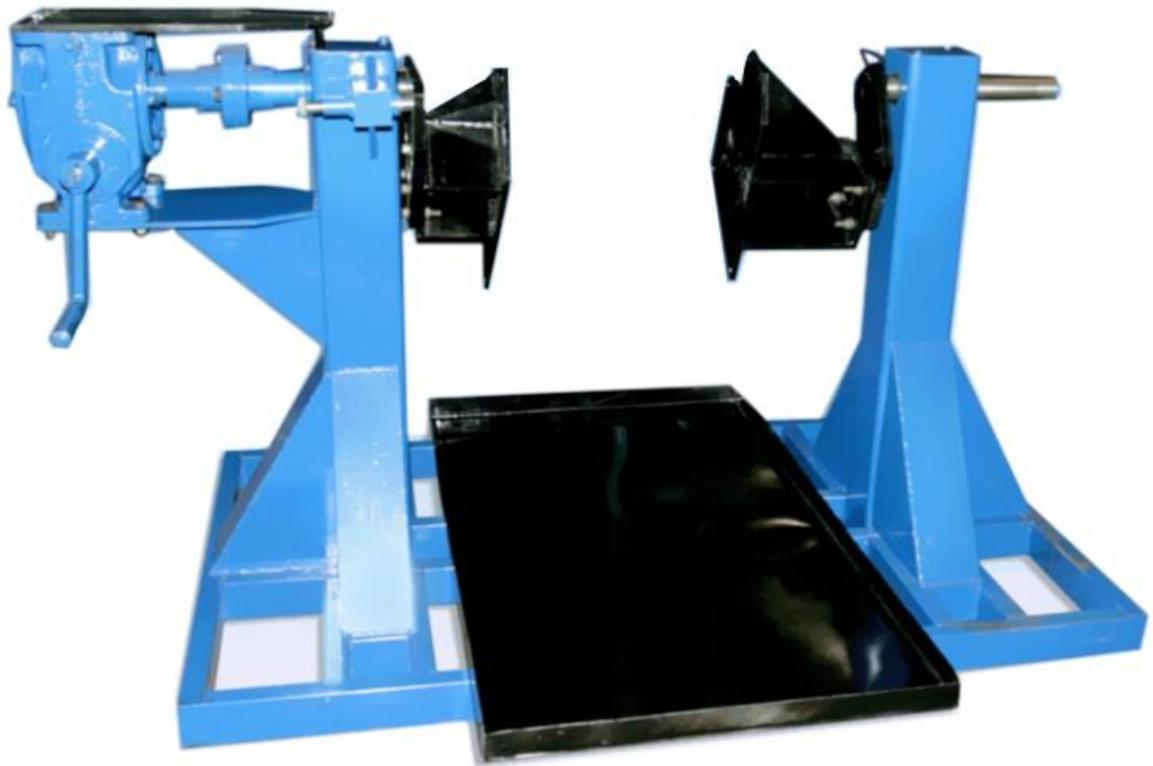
Стенд для разборки-сборки Р-650
